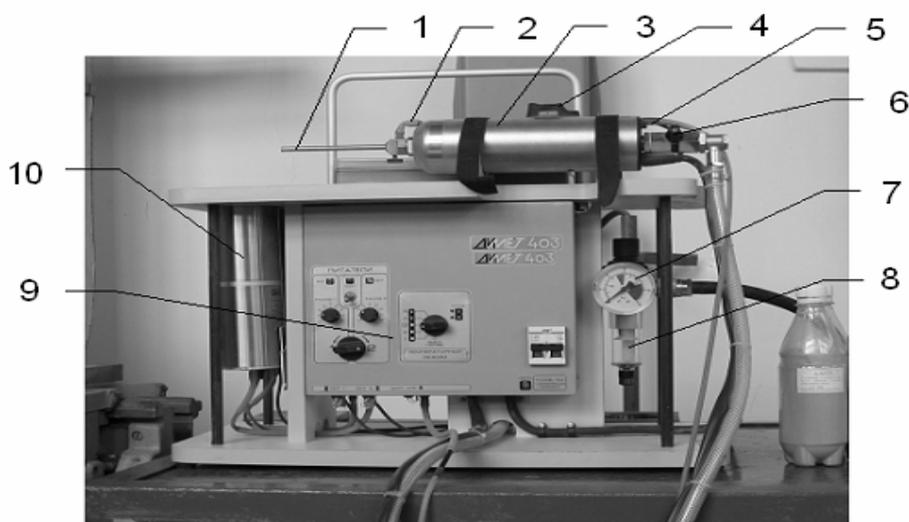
Общий вид комплекта «ДИМЕТ-403» для сверхзвукового газодинамического напыления порошковых материалов: 1 – сопло СК-6; 2 – силиконовый переходник; 3 – напылитель ДМ-43; 4 – кнопка подачи порошка; 5 – трубка подачи порошка; 6 – пневмокран напылителя; 7 – манометр; 8 – фильтр-регулятор N204-DOO; 9 – блок контроля и управления БКУ-03; 10 – питатель ПВ-43.
